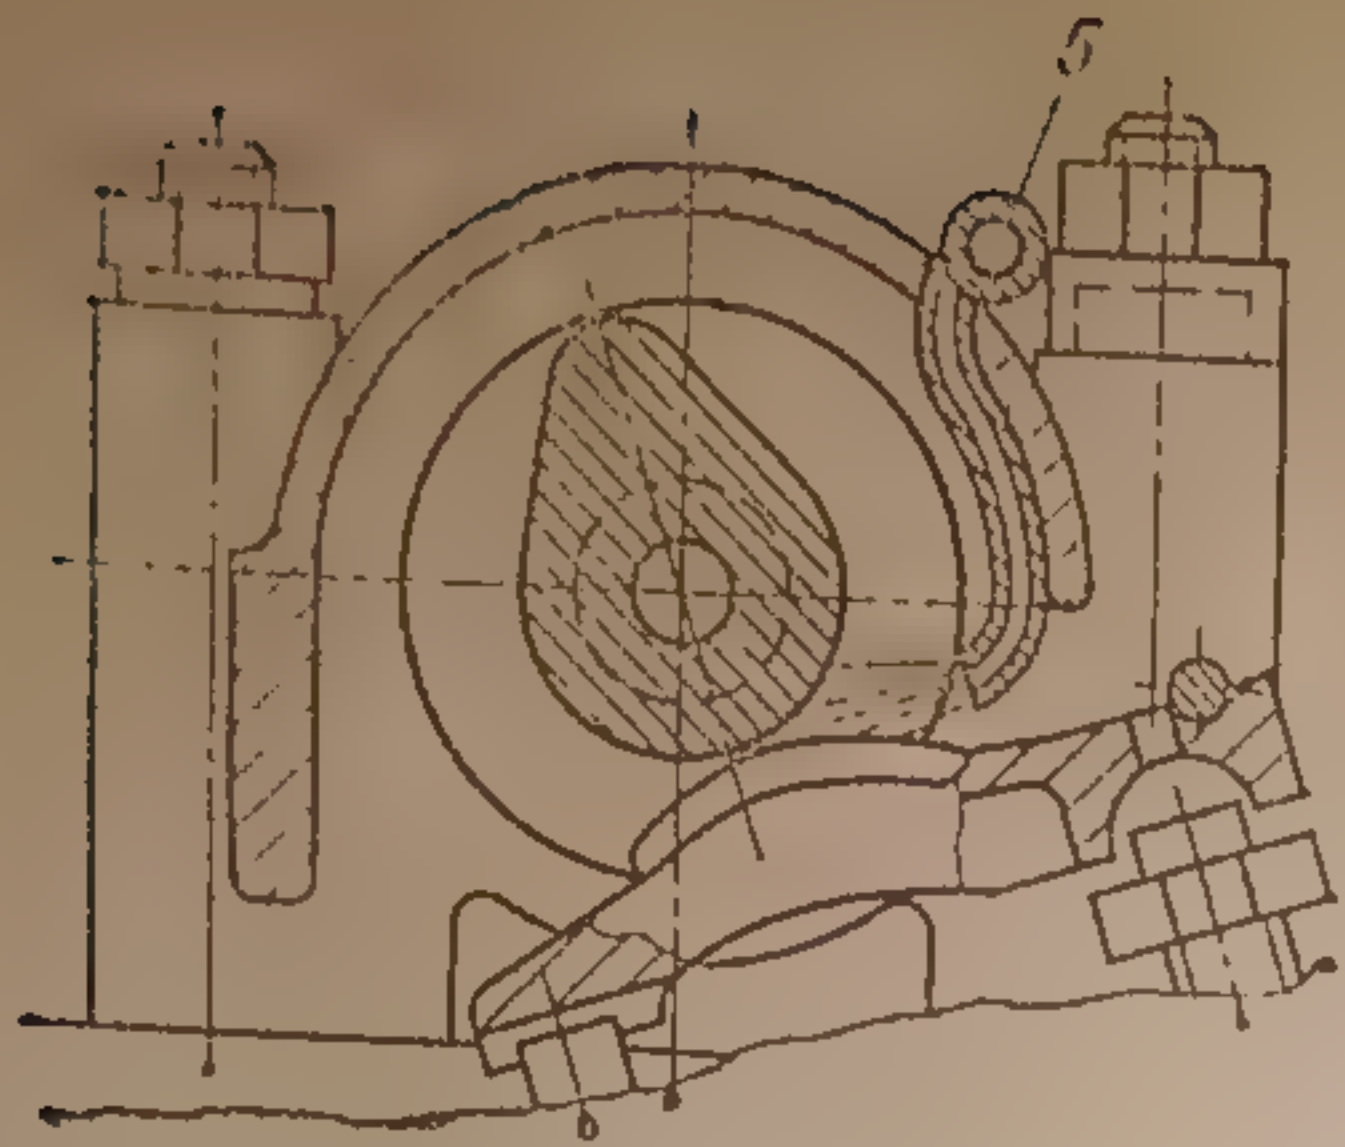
Подача масла в системе В. М. Загорько и Э. М. Кожухова: 1 — маслородводящий канал; 2 — центральная шпилька крепления корпуса подшипников распревала; 3 — распределитель; 4 — корпус подшипников; 5 — маслородводящая трубка
